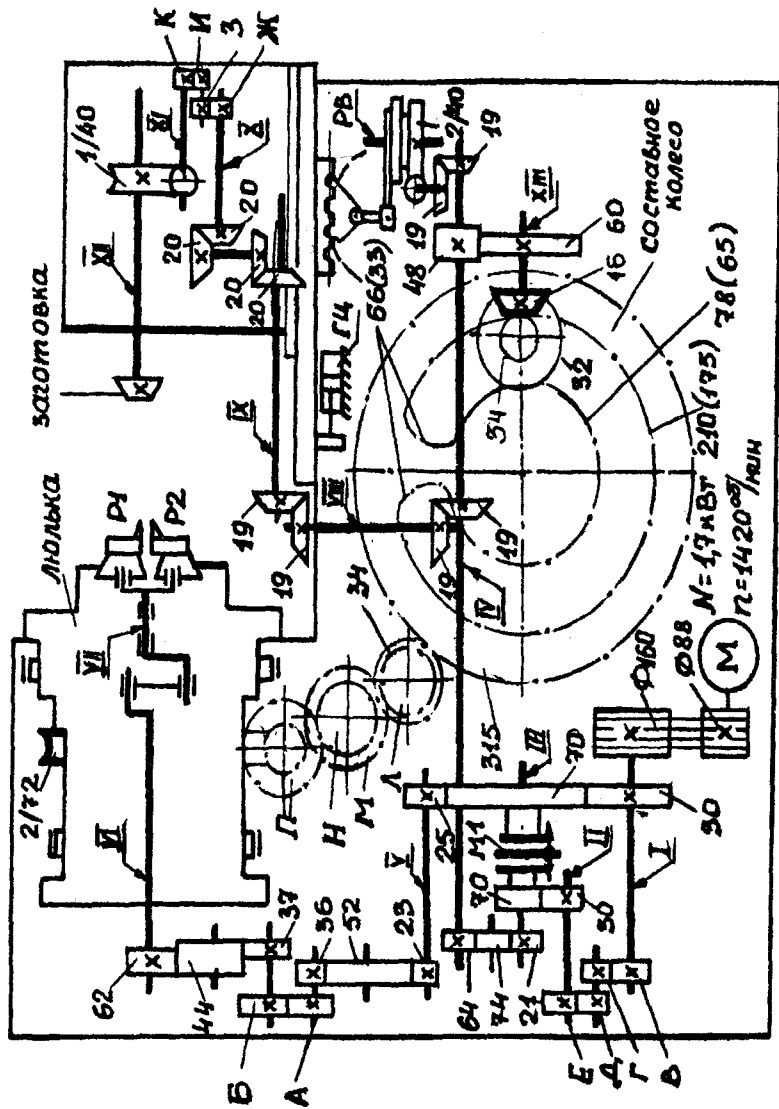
Кинематическая схема зубострогального станка модели 5П23Б
